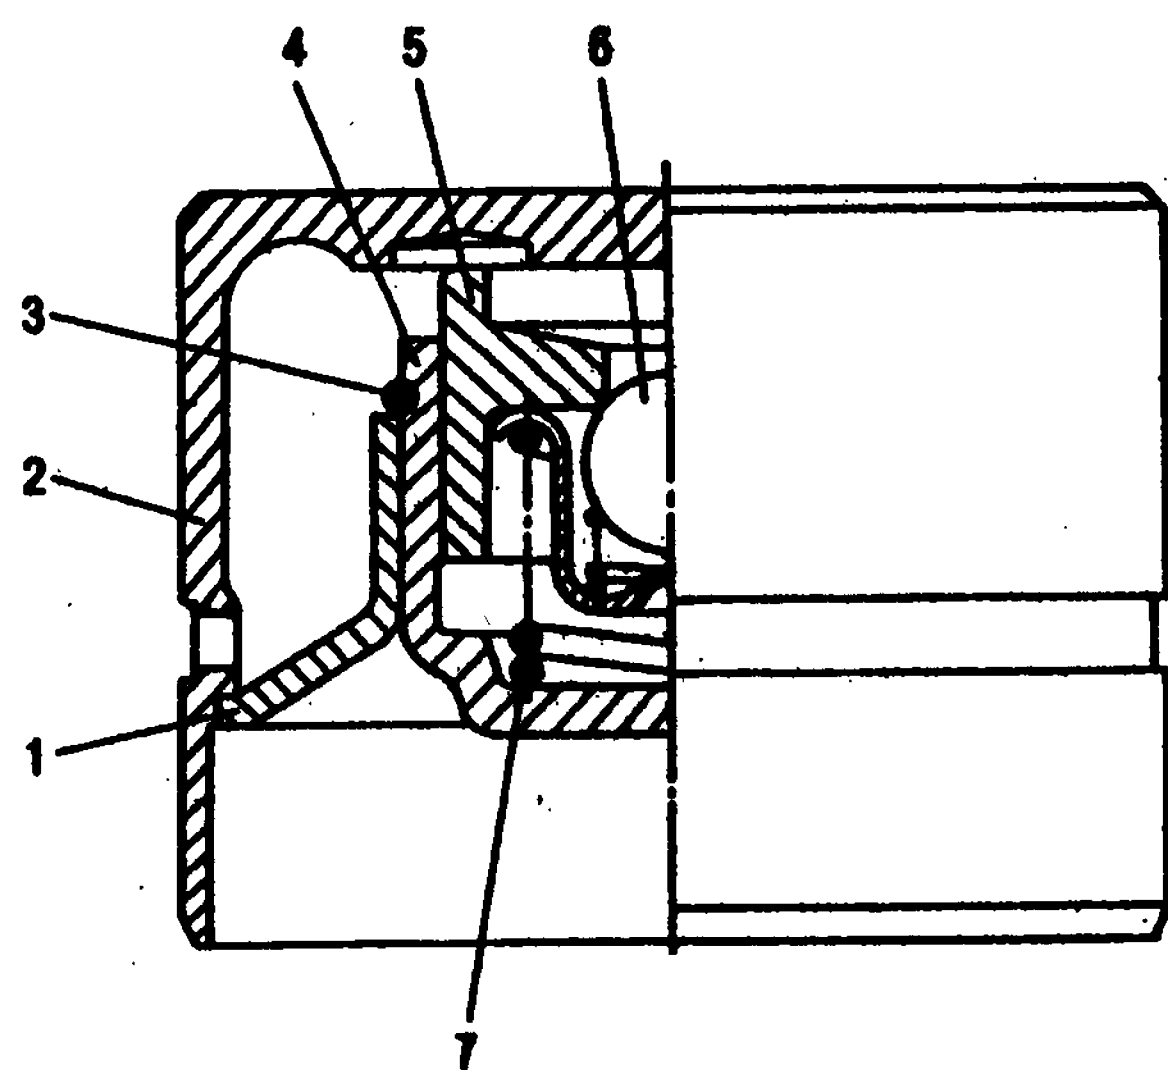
Гидротолкатель: 1 - направляющая втулка компенсатора; 2 - корпус гидротолкателя; 3 - стопорное кольцо; 4 - корпус компенсатора; 5 - поршень компенсатора; 6 - обратный шариковый клапан; 7 - пружина
